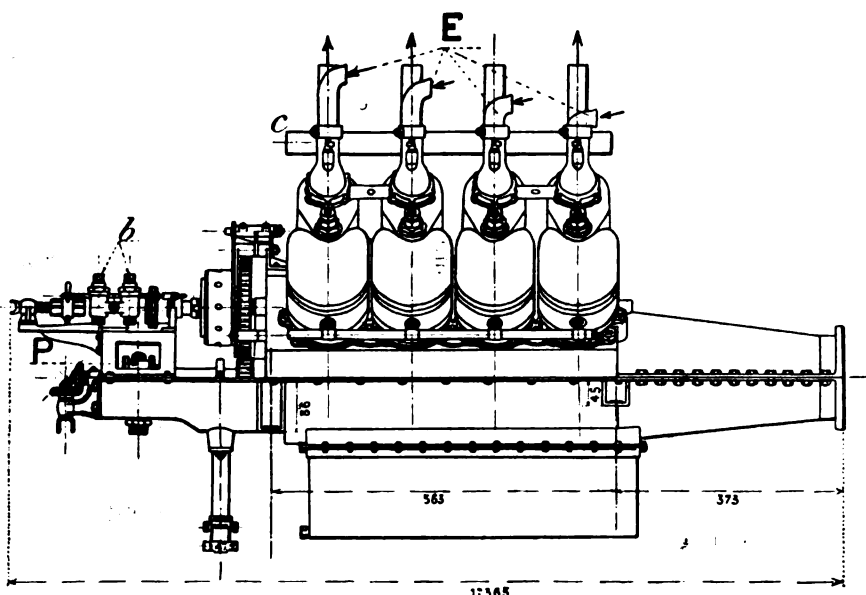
Zeichnung des Motors »Antoinette«. Seitenansicht. b Pumpen für Öl und Benzin. P Wasserpumpe.
